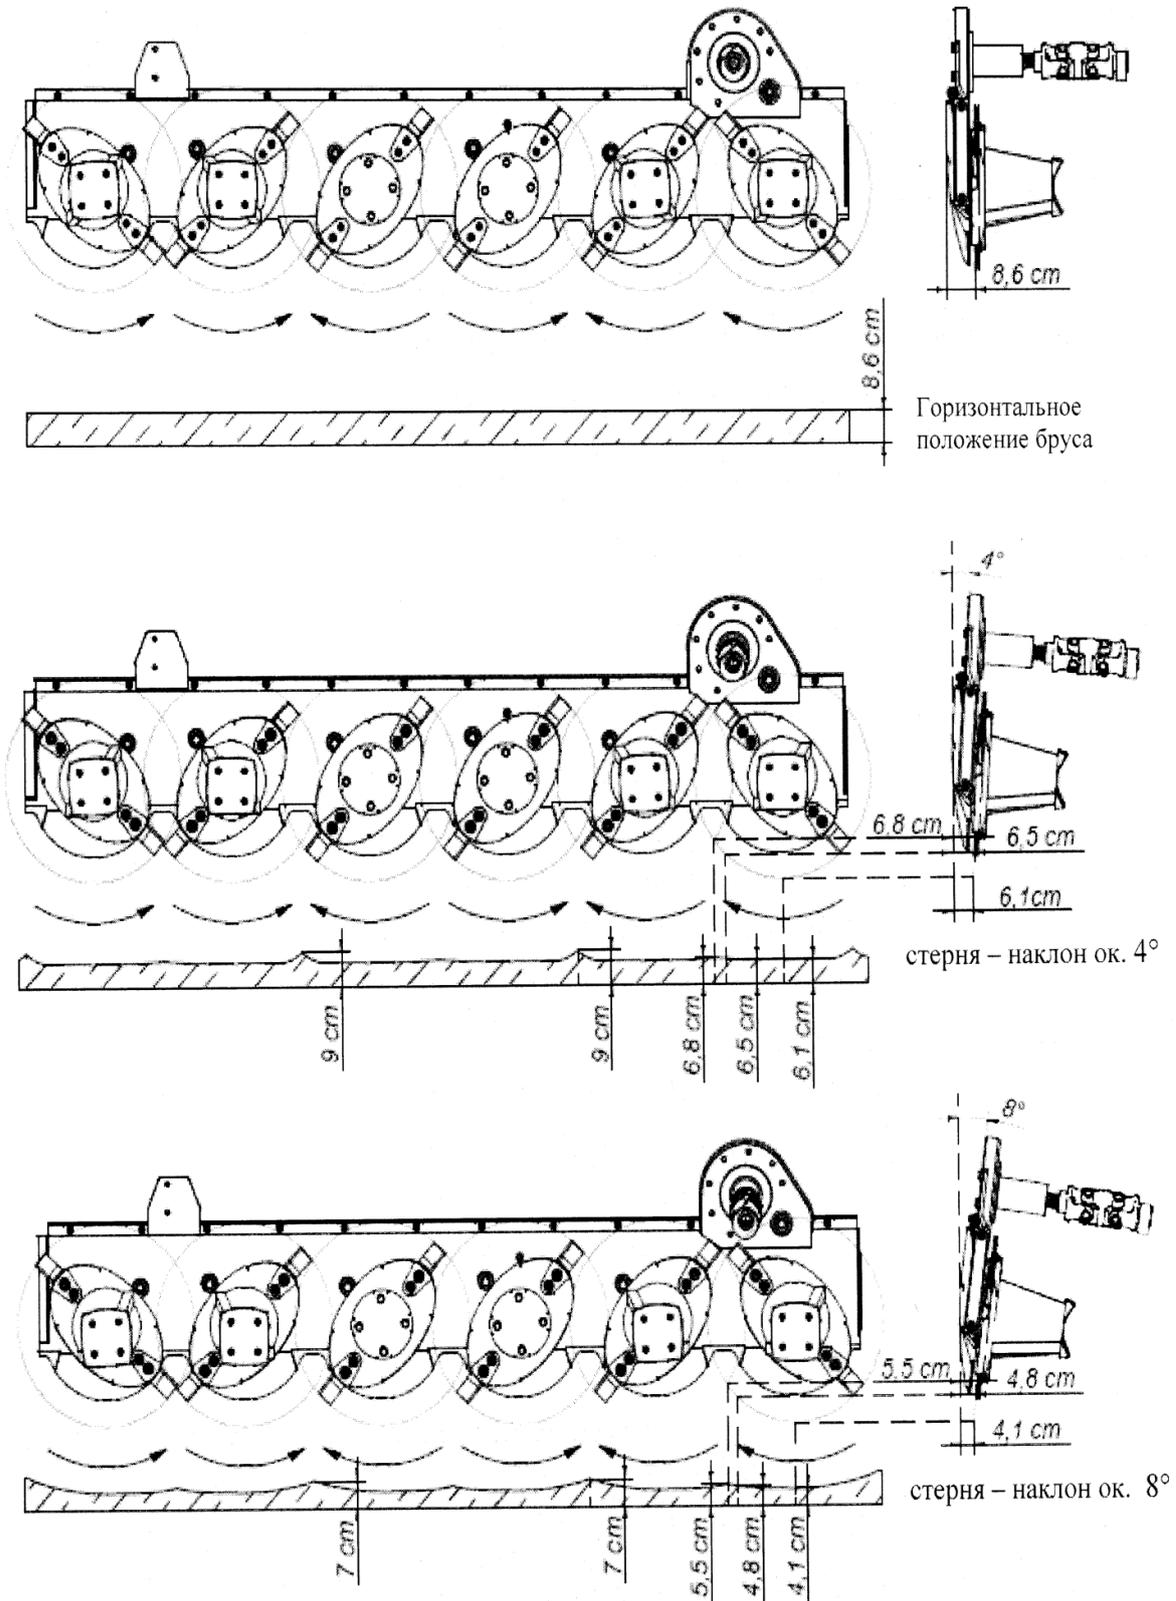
Рельеф стерни при углах режущего бруса 0, 4 и 8 градусов
